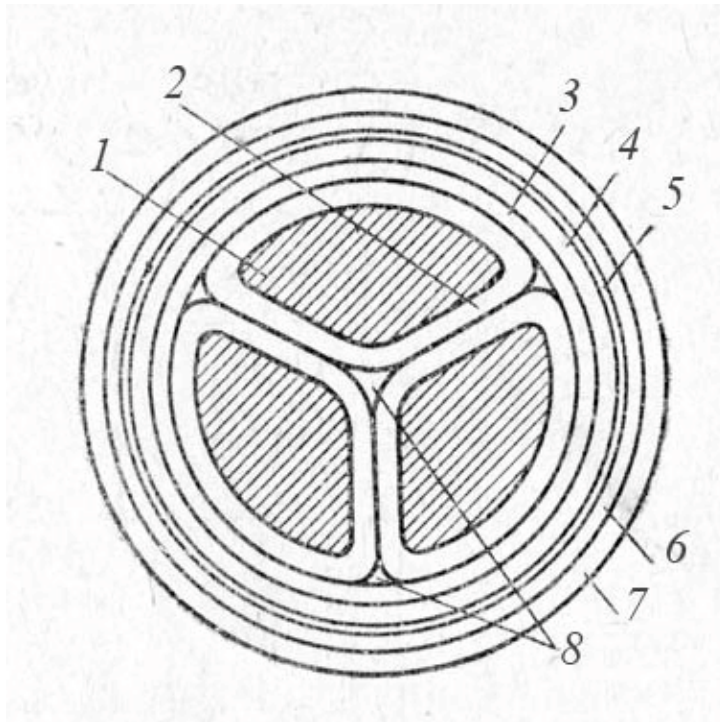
Кабель с бумажно-масляной изоляцией на 10 кВ: 1 – медная токопроводящая жила; 2 – фазная изоляция; 3 – поясная изоляция; 4 – свинцовая оболочка; 5 – подушка под броней; 6 – броня; 7 – защитные покровы; 8 – заполнение
